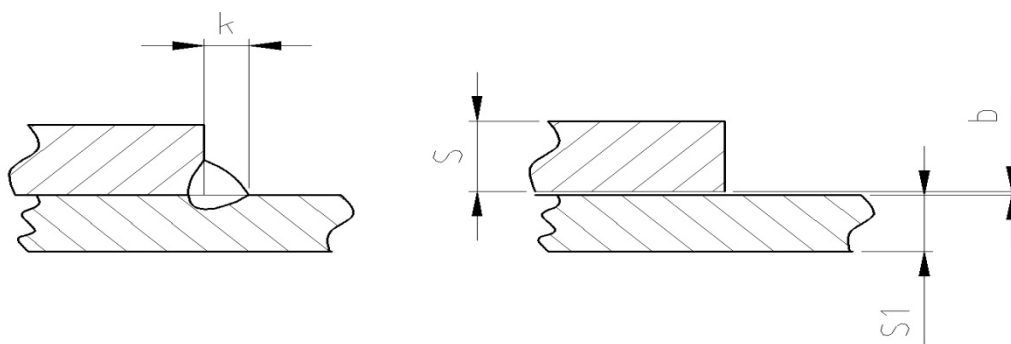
Эскиз сварного соединения I
